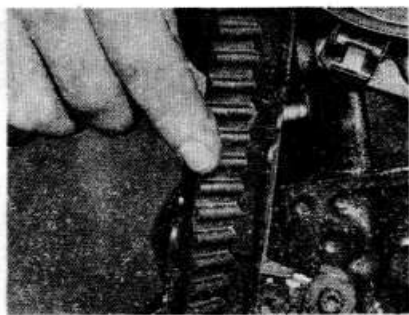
Проверка натяжения ремня скручиванием на 90° между большим и указательными пальцами — для двигателей 2,0 л
